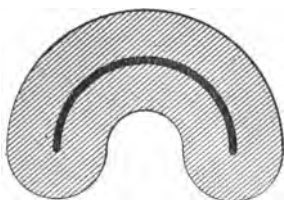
Coupe d'un tube Serpollet; échelle de 1/2.
